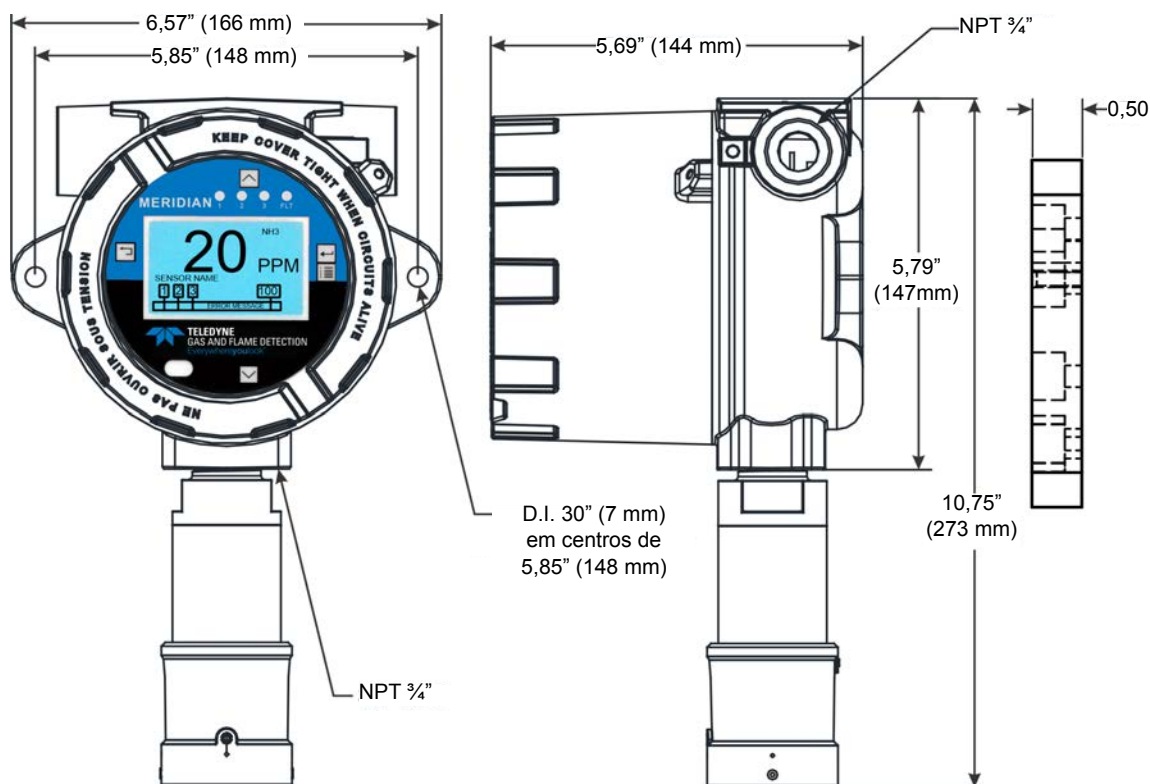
Dimensões de montagem do dispositivo - alumínio e aço inoxidável
